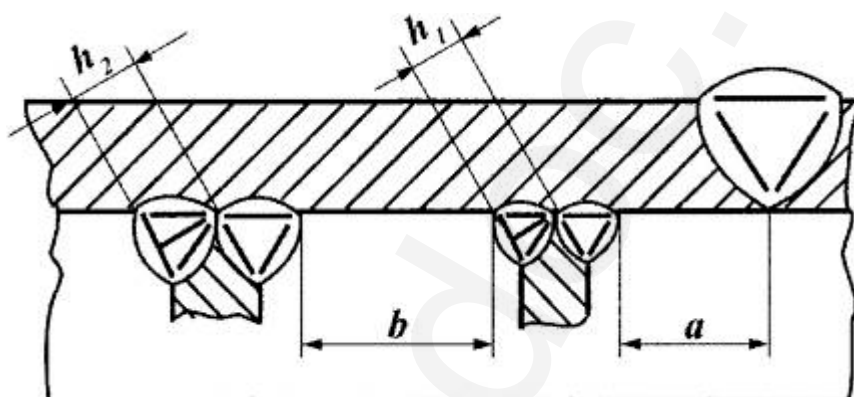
Расположение сварных соединений приварки деталей к оборудованию и трубопроводам
